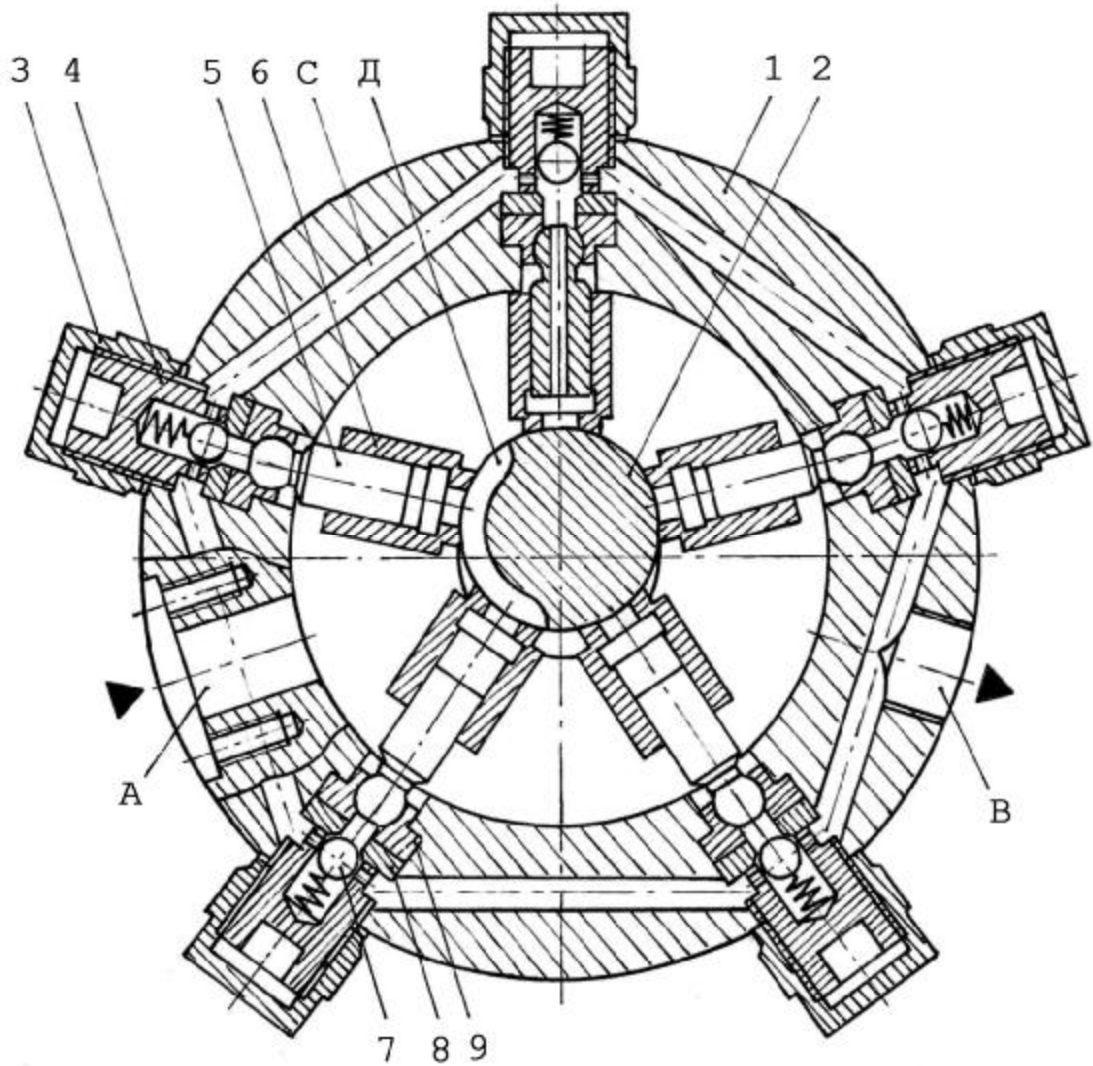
Гидронасос 50HP 32/2: 1 – корпус, 2 – эксцентриковый вал; 3 - колпачок; 4 – корпус клапана; 5 – поршень; 6 – цилиндр; 7 – обратный клапан; 8 – седло; А – канал подачи рабочей жидкости; В – канал нагнетания; С - коллектор нагнетания; Д – паз для подвода рабочей жидкости.
